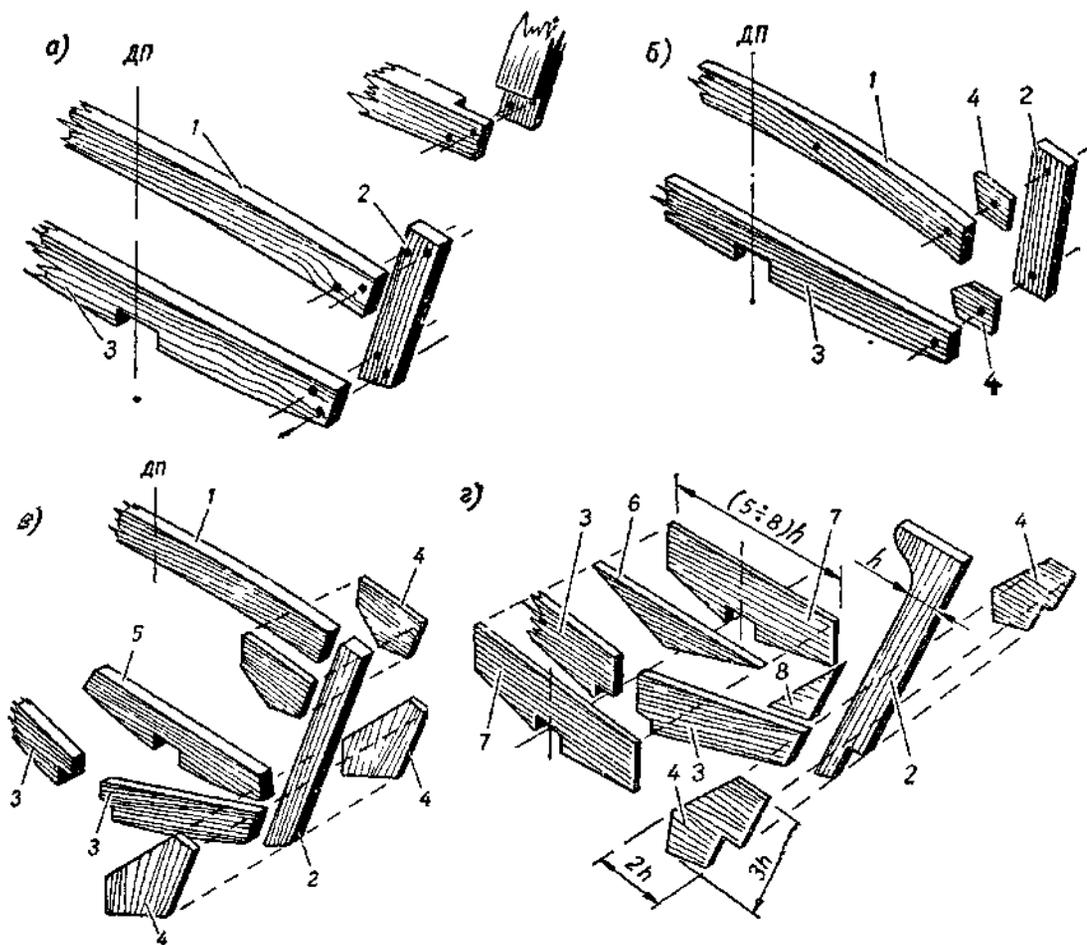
Варианты сборки шпангоутных рамок; а — внахлестку (и вариант с дрезкой вполдерева); б — с применением одинарных книц; в — с флором и двусторонними кницами; г — с фанерными двусторонними флорами и кницами с заполнителем.
